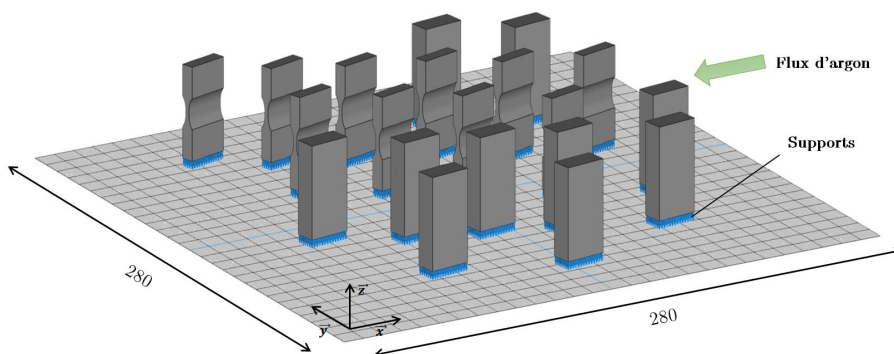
Plateau de fabrication des éprouvettes plates et des pavés droits
